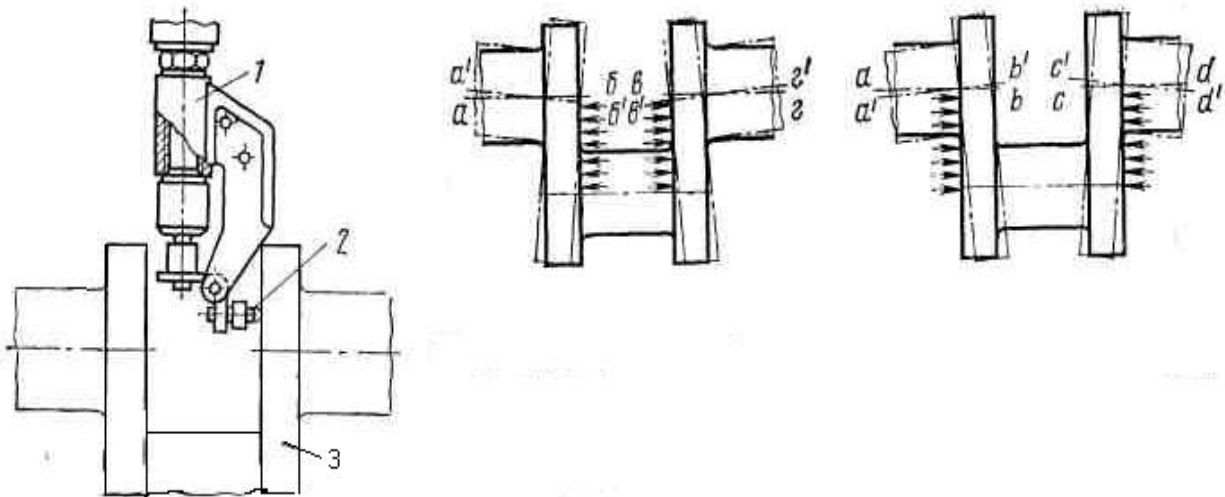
Виправлення сталевого колінчастого вала методом механічного наклепу:
